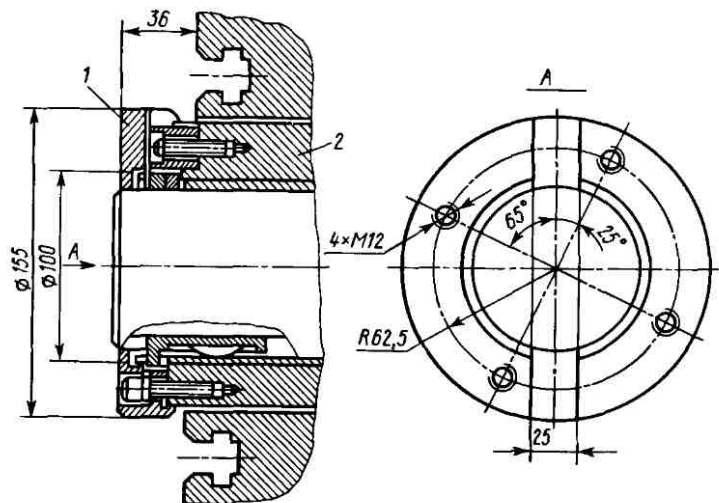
Установка и закрепление лобовой фрезы на фрезерном шпинделе станка
